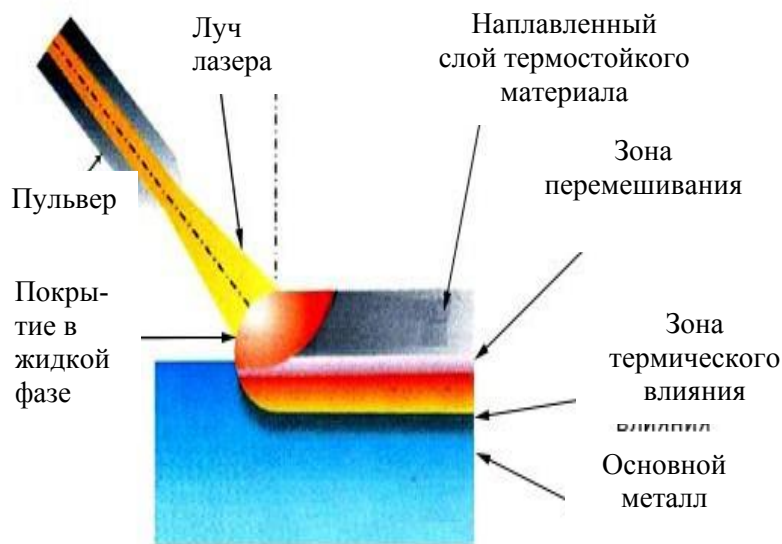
Процесс лазерной наплавки на внутреннюю поверхность трубы:
